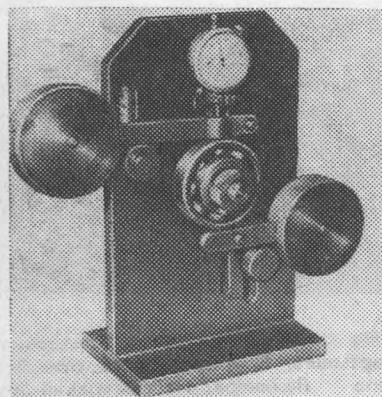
Приспособление для измерения радиальных зазоров в шариковых подшипниках
